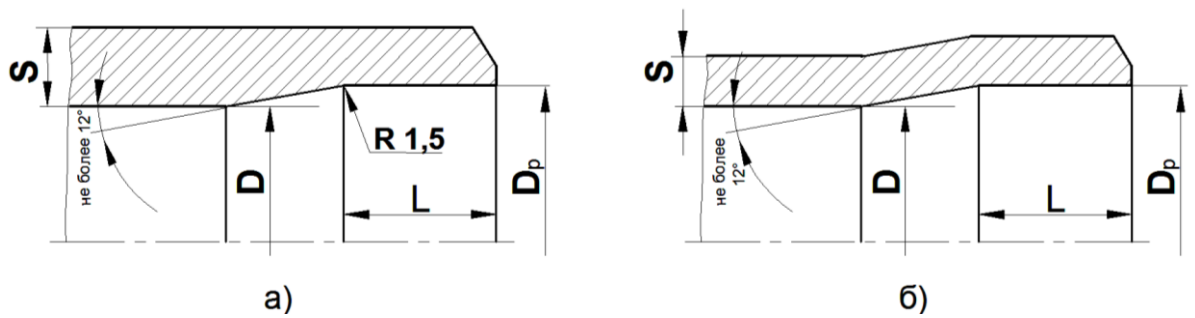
Схемы цилиндрической расточки (а) и калибровки (раздачи) (б) концов труб (патрубков) под стыковые сварные соединения с односторонним швом.
